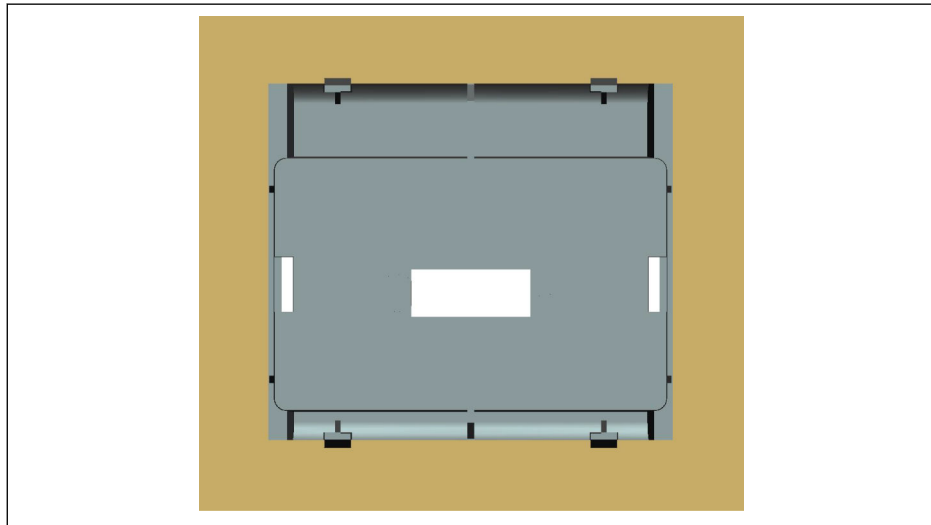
Pousser la plaque de montage dans l'ouverture (vue arrière)
